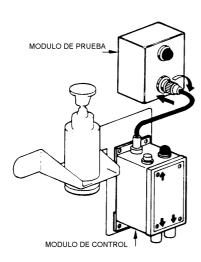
INSTALE EL CONJUNTO DEL MODULO DE PRUEBA
